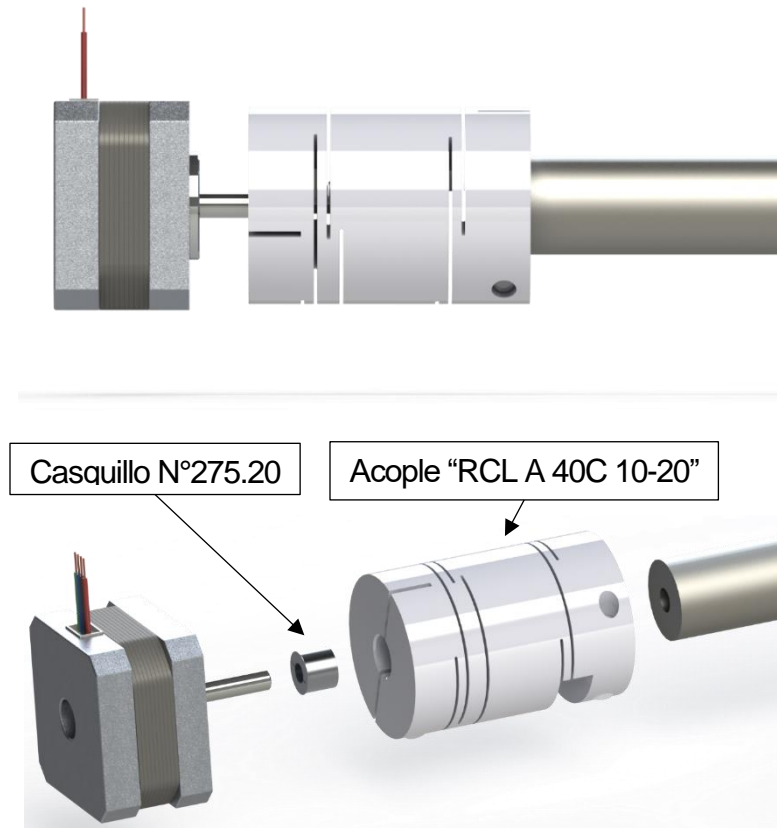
Arriba, vista lateral del conjunto motor, casquillo, acople y barra. Abajo, vista explosionada del conjunto
